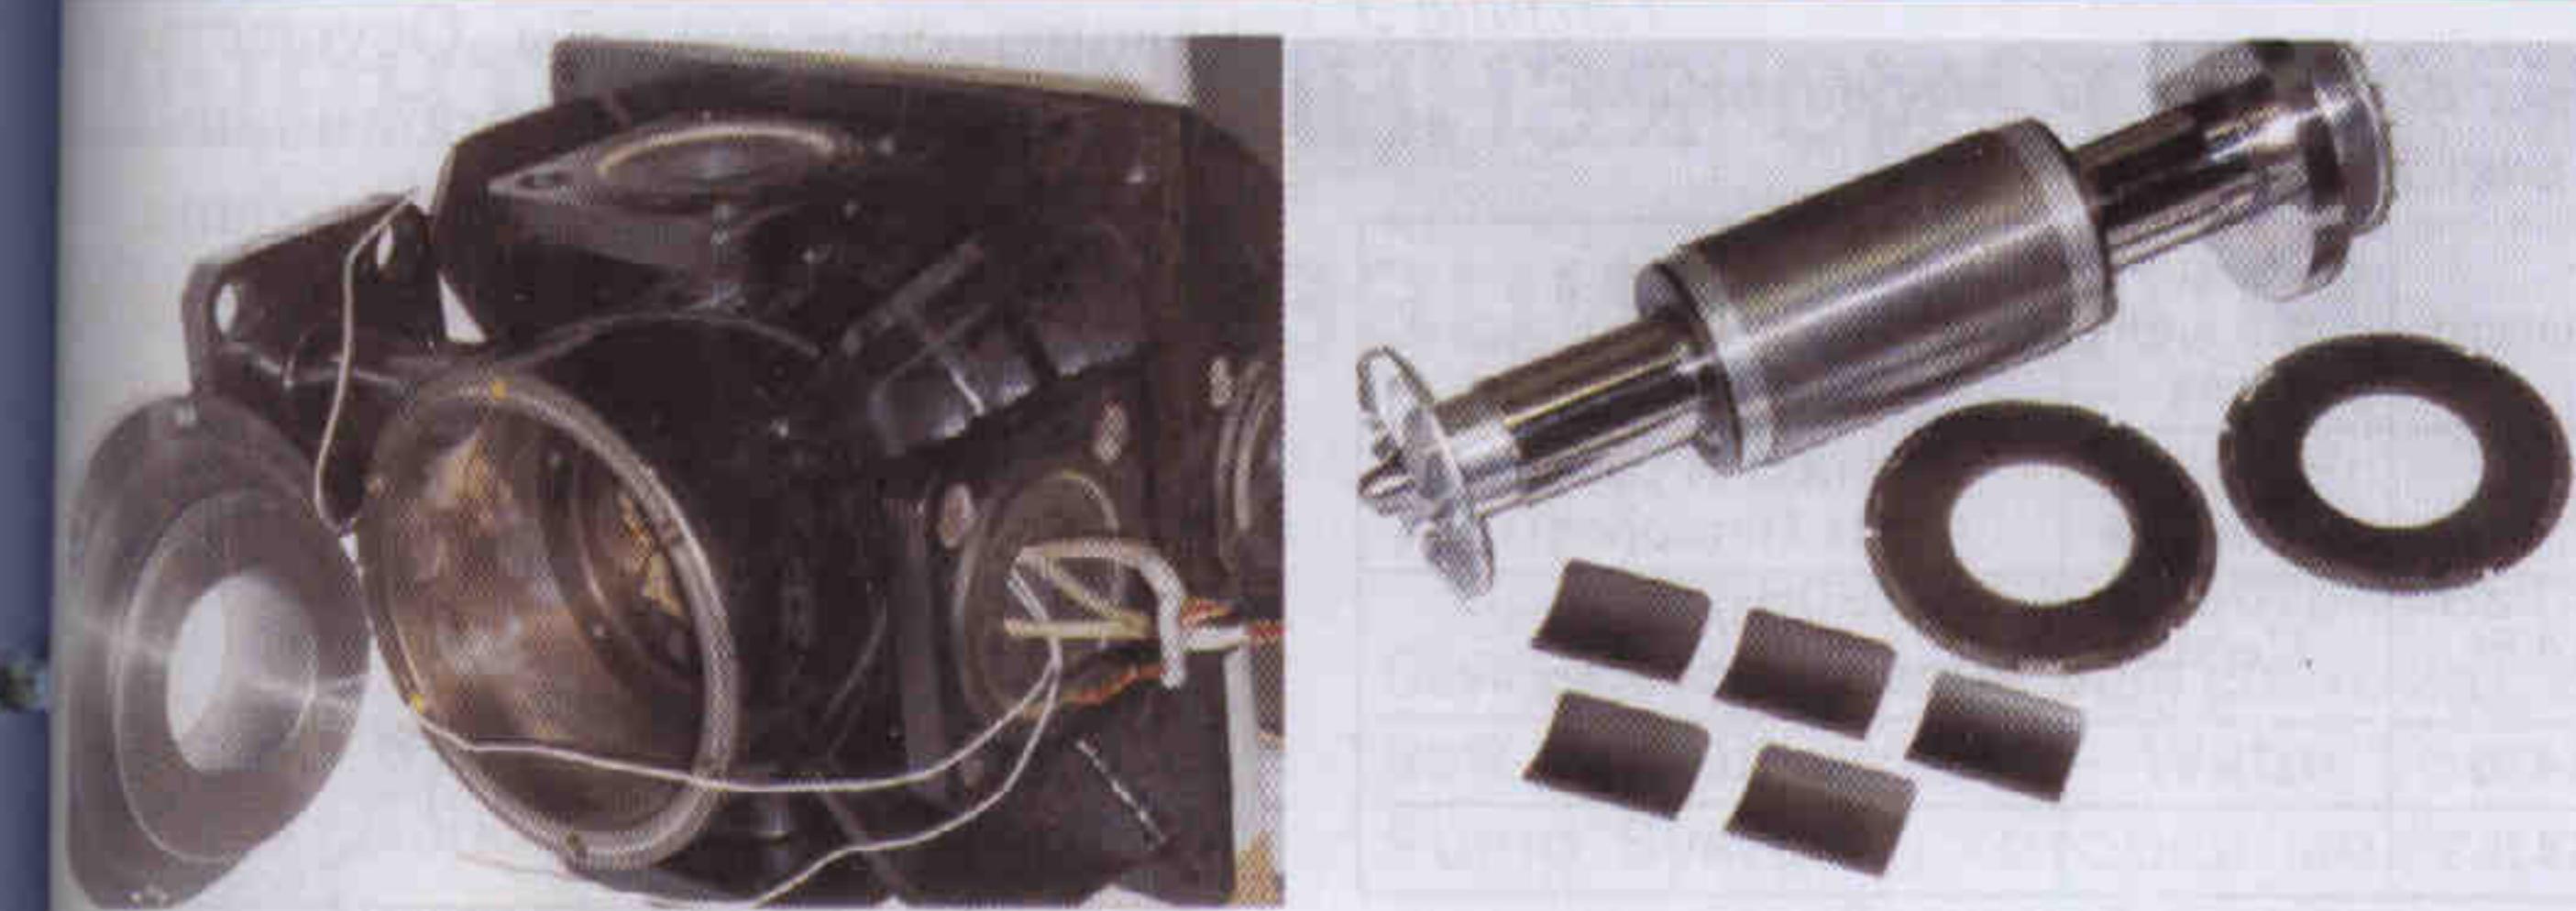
Корпус и ротор турбокомпрессора ТК-0,03
